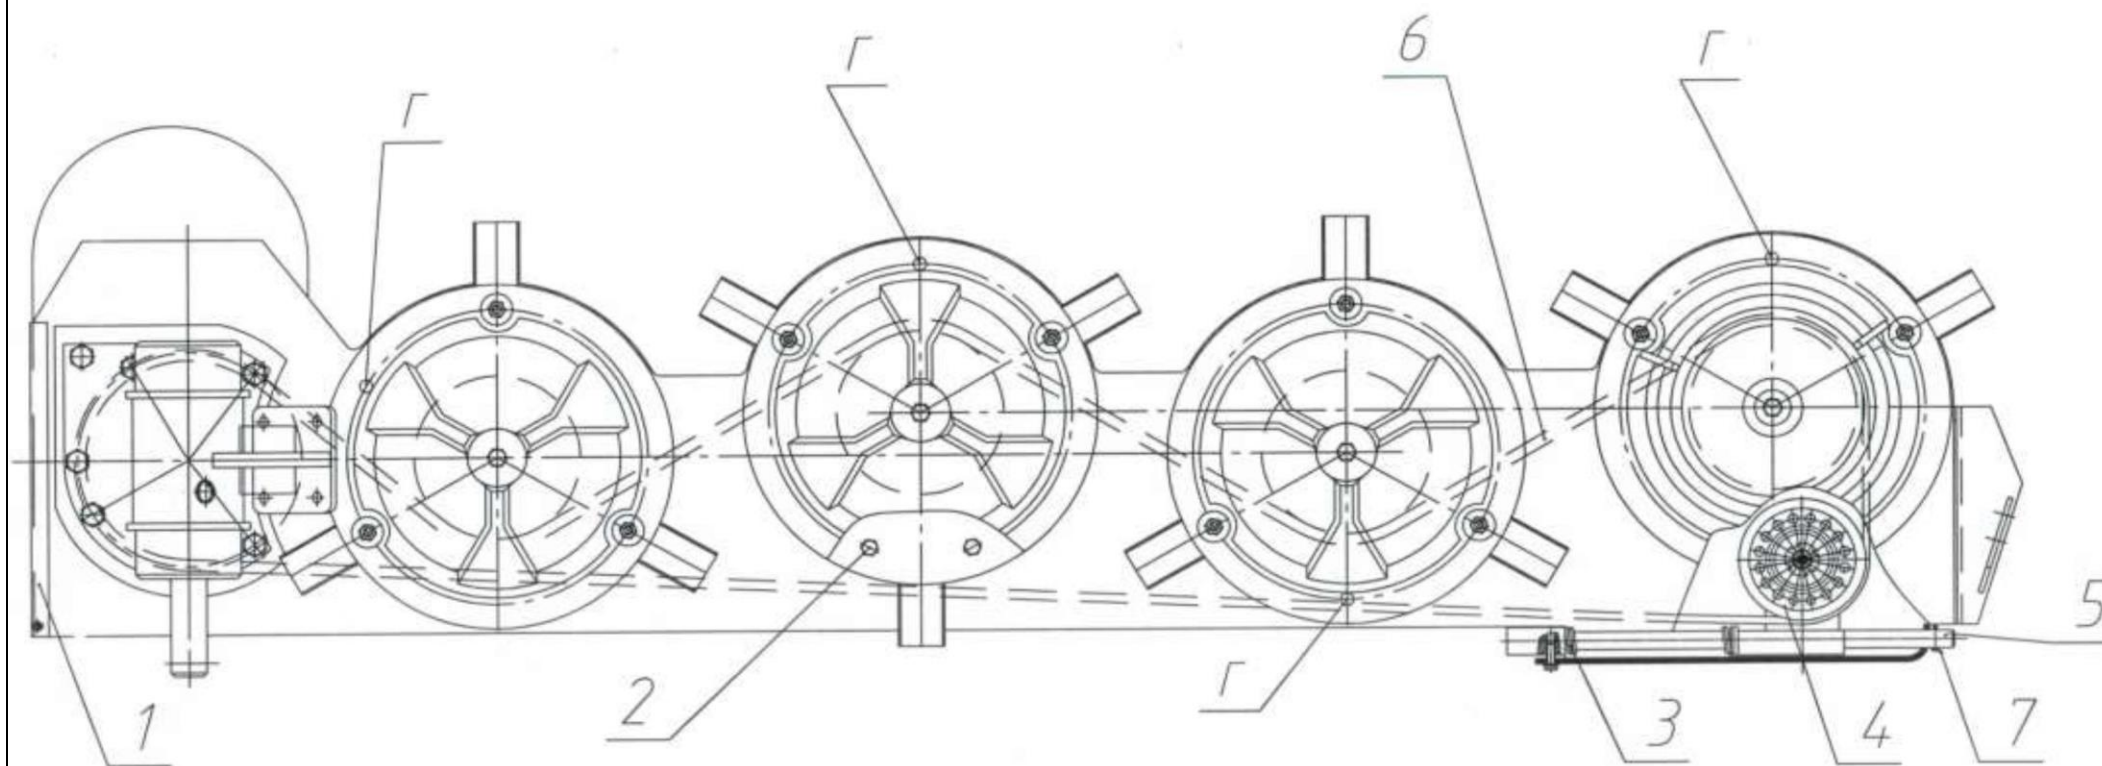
а Режущий брус косилки KPP-1,85M, KPP-1,9
